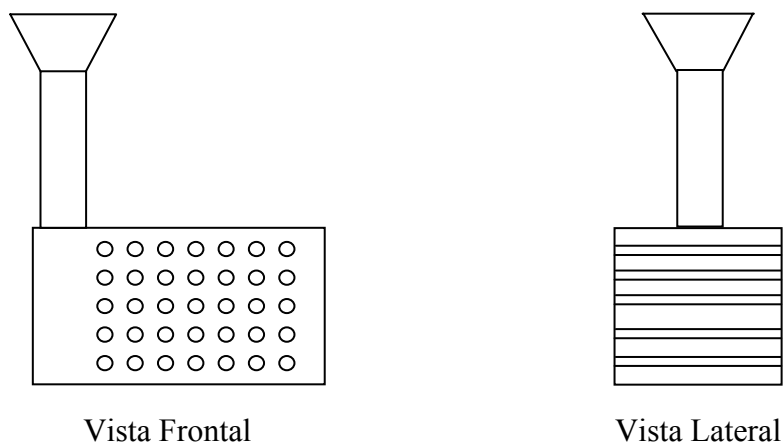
Caixa de Preenchimento (Fill Box)
